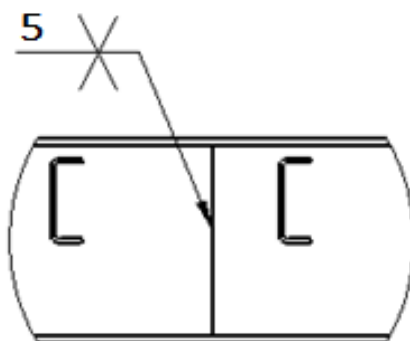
Soldadura a Tope Viga Principal
